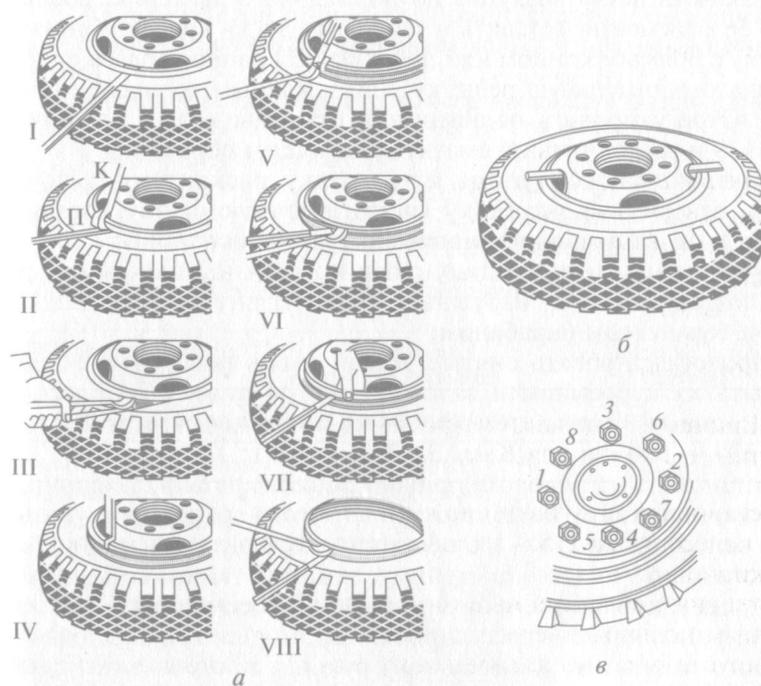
Демонтаж шины с обода колеса автомобиля ЗИЛ-130;
